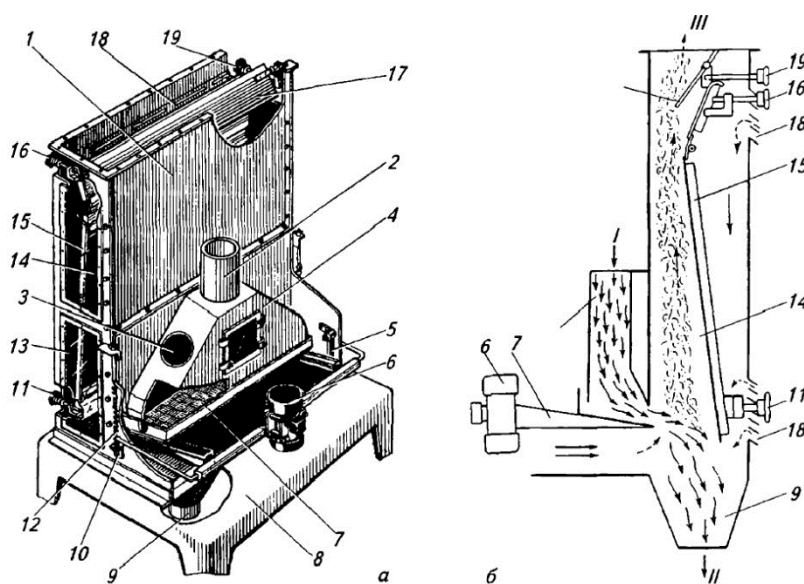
Воздушный сепаратор РЗ-БАБ:
